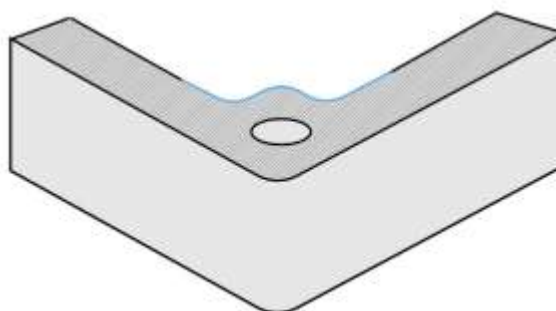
Утолщения и скругления внутри корпуса позволяют уменьшить напряжение вокруг отверстия
